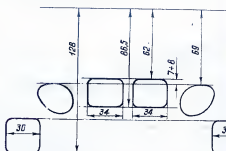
Развертка цилиндра двигателя ИЖ-56, подготовленного для соревнований.
